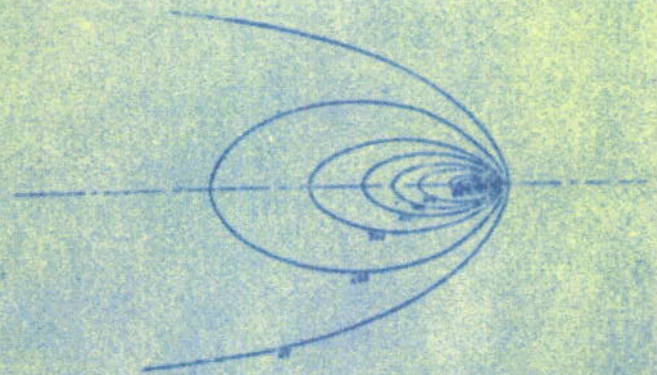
Isothermes à un instant donné, pour la soudure à l'arc de l'acier doux (plaque 10 mm).
